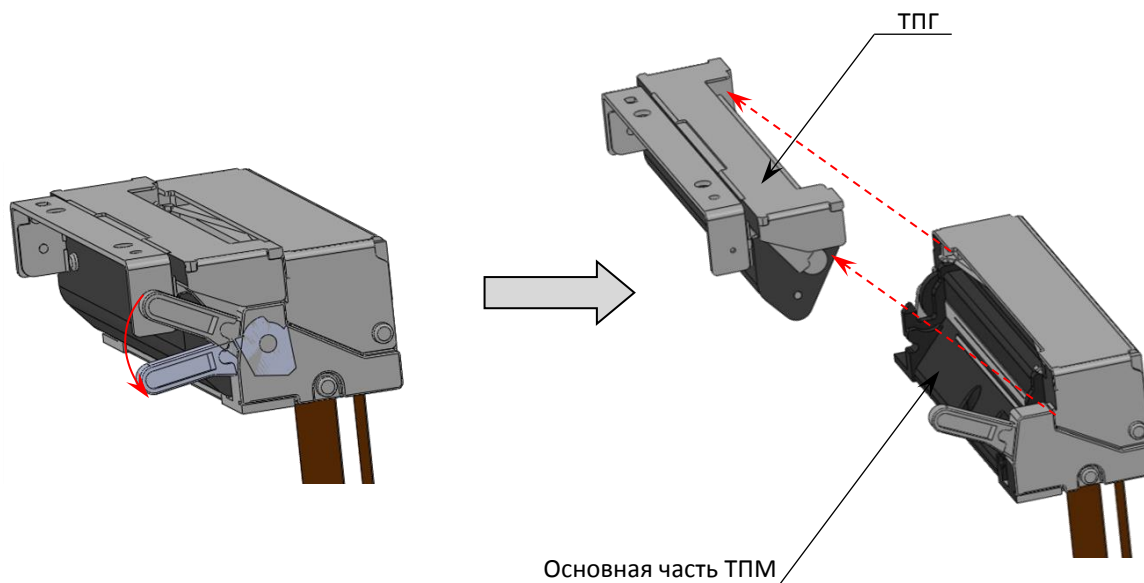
Термопечатающий механизм SII CAPD245E-E
